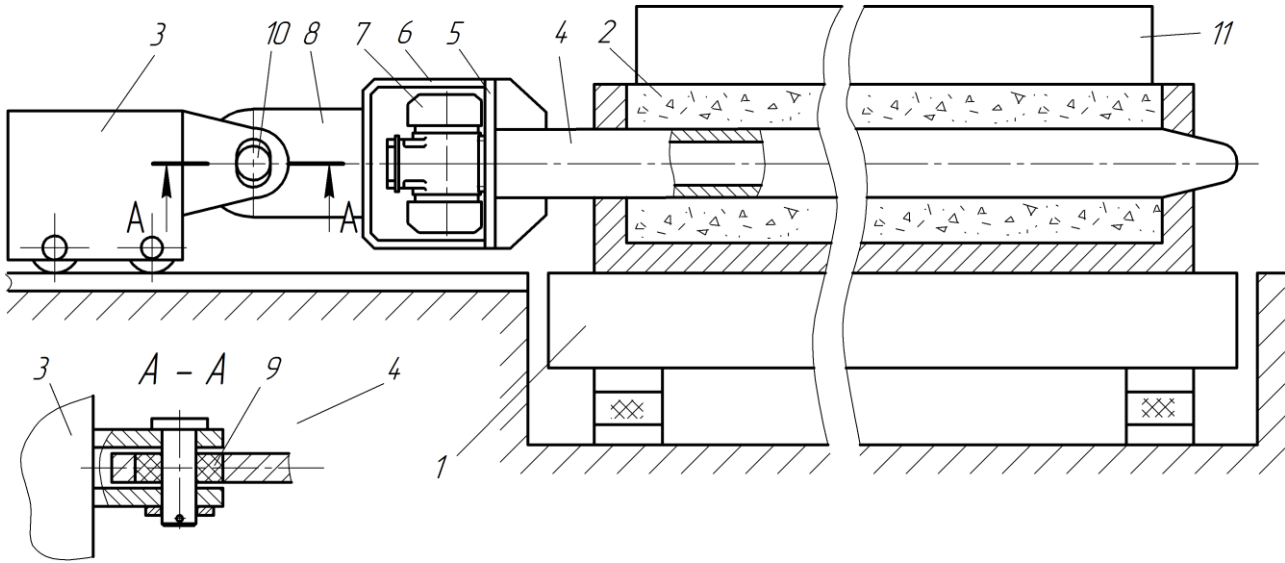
Схема установки для формования многопустотных панелей перекрытий с пригрузом.
